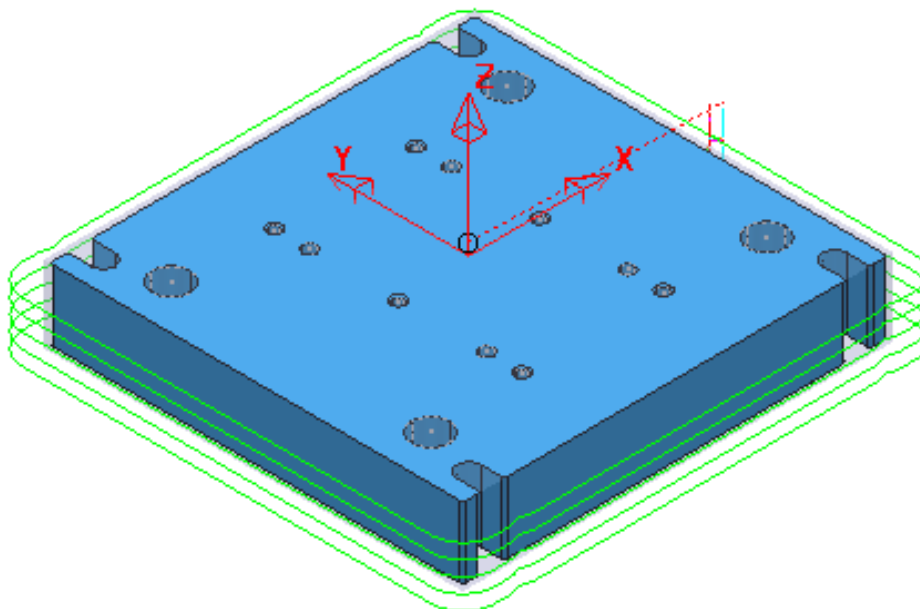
010 фрезерная (обработка боковых поверхностей)
